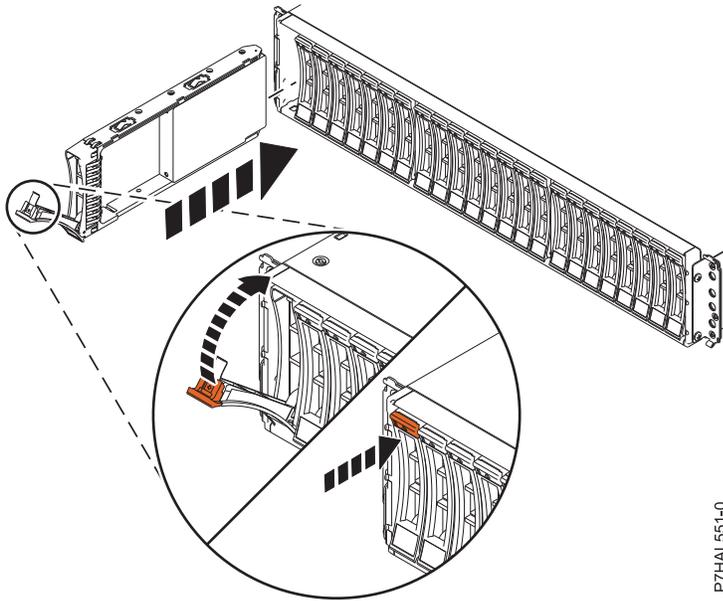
Plattenlaufwerk im 5887 Plattenlaufwerkgehäuse installieren oder austauschen
